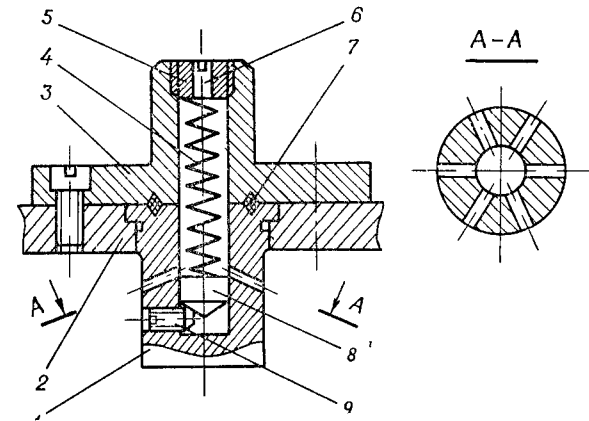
Схема пуансона с автоматической смазкой рабочей поверхности
